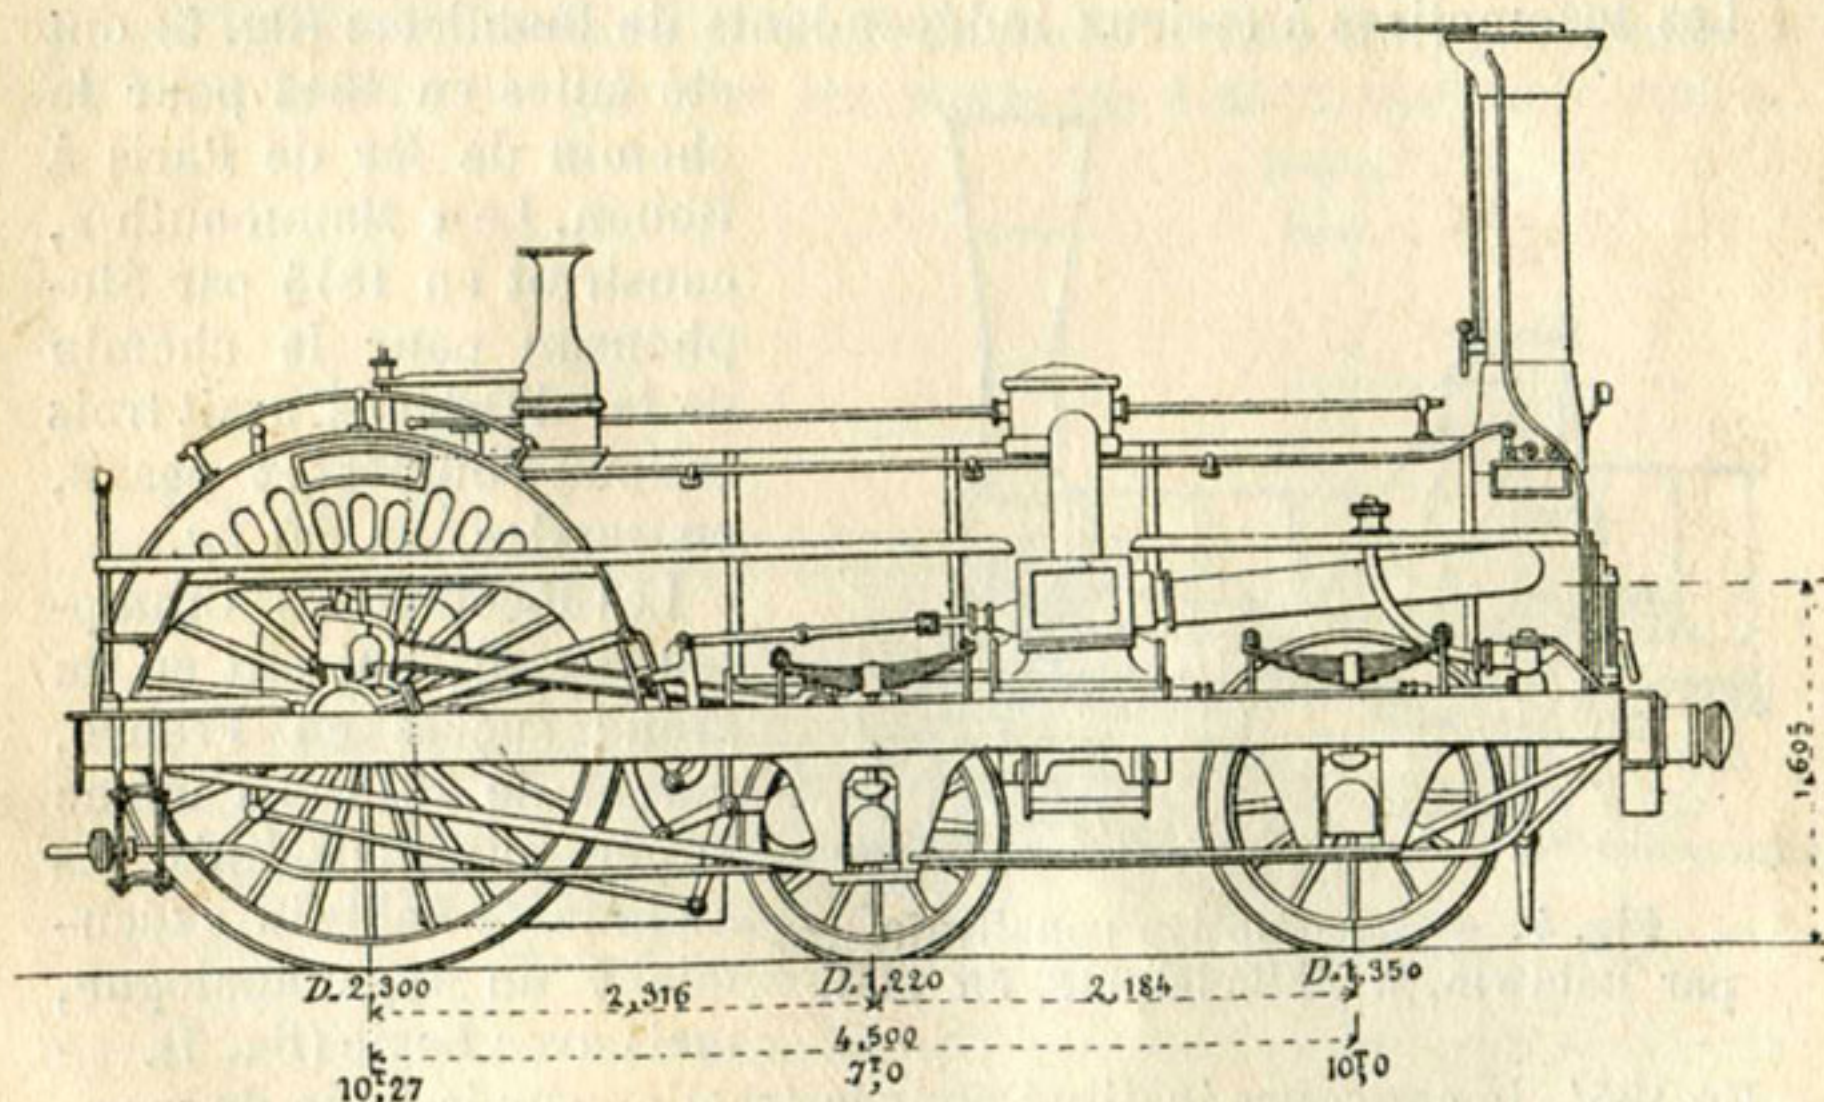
Locomotive Crampton des chemins de fer de l'Est; type de 1852. (D'après M. Demoulin.)
